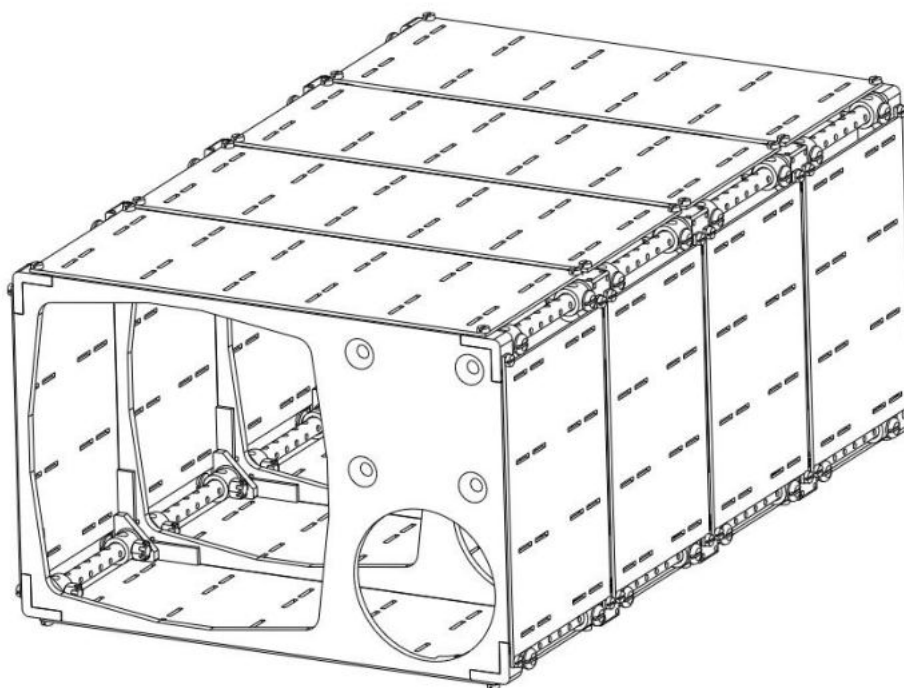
Конструкция корпуса разрабатываемой универсальной космической платформы
